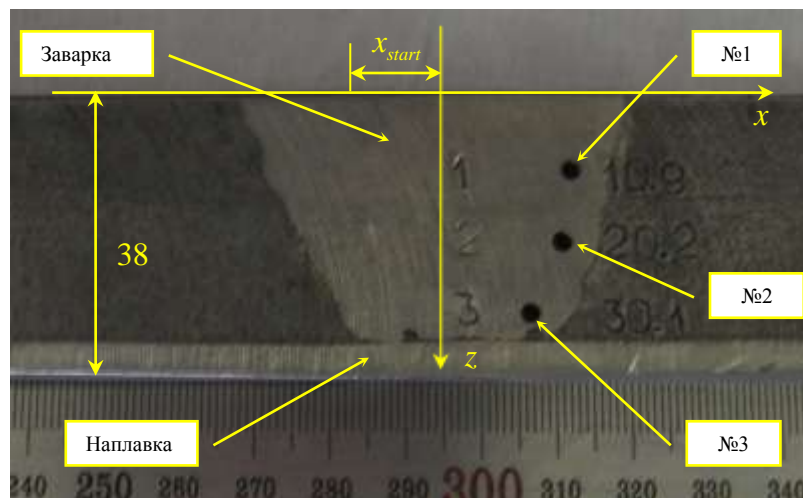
Схема образца трубопровода Ду800 толщиной 38 мм с никельсодержащей заваркой и тремя отверстиями бокового сверления диаметром 2 мм.
